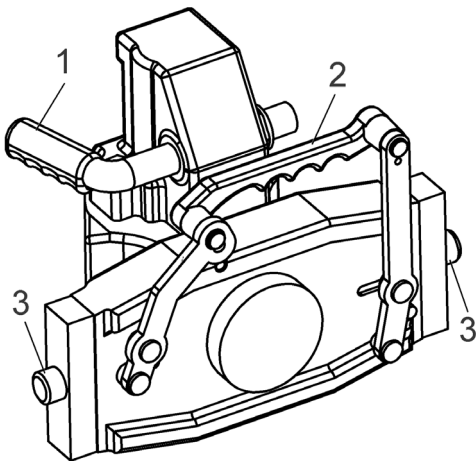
Тяглово-зчіпний і причіпний пристрій
